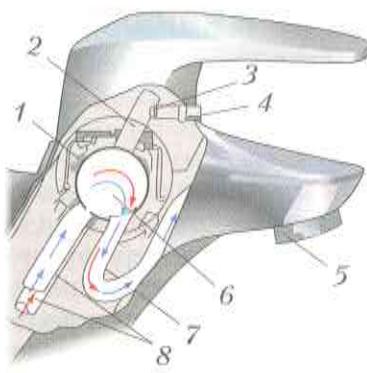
Устройство однорычажного смесителя с шаровым механизмом:
